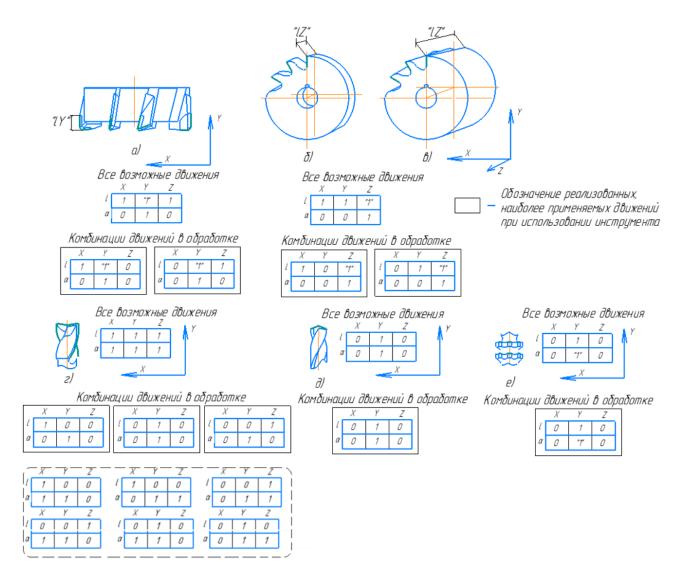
Комбинации движений инструмента: а) торцевой фрезы; б) дисковой фрезы; в) цилиндрической фрезы; г) концевой фрезы; д) сверла; е) круглой протяжки
